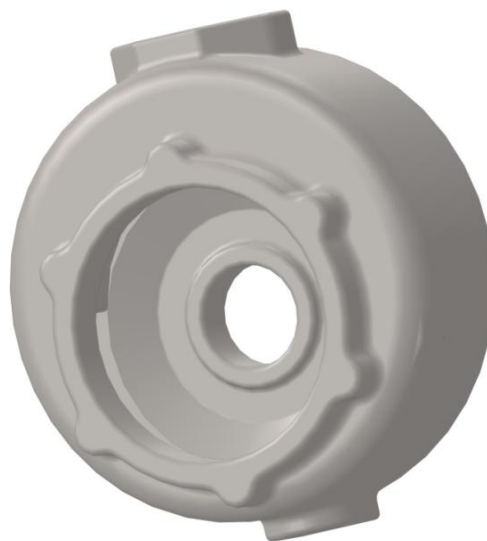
3D модель заготовки корпусу ПИМ 16.101
